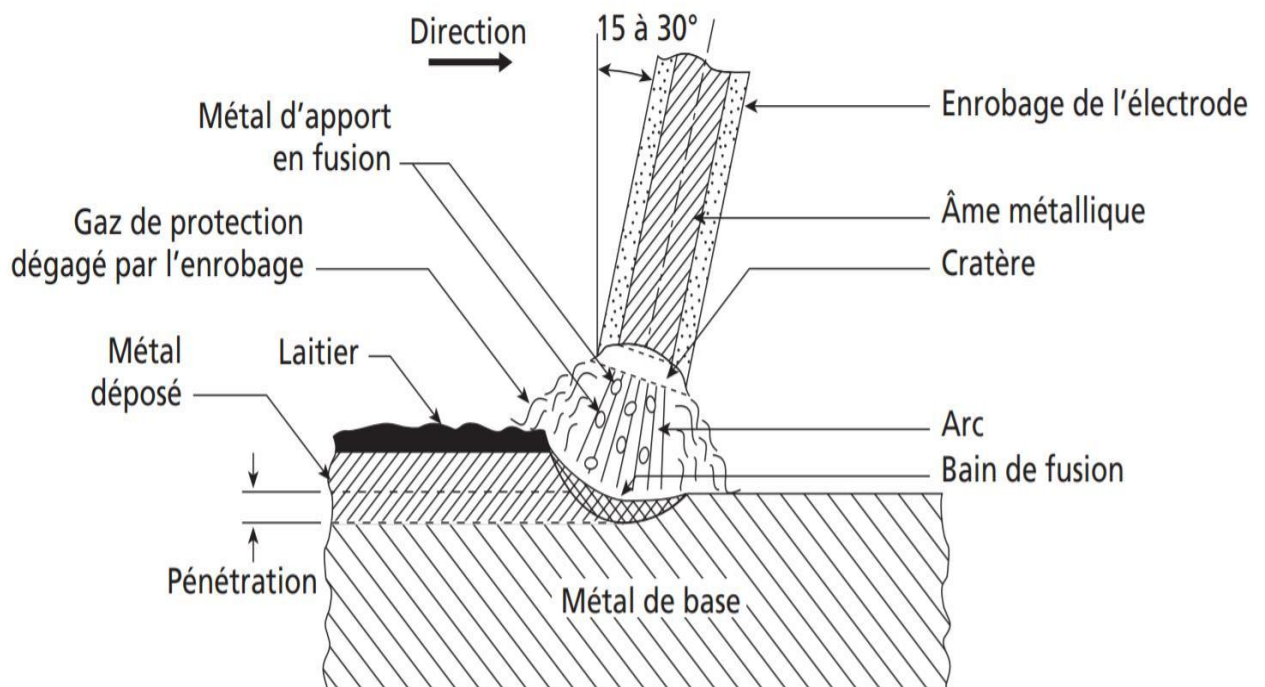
Principe de soudage à l'arc avec électrode enrobée (SMAW)
